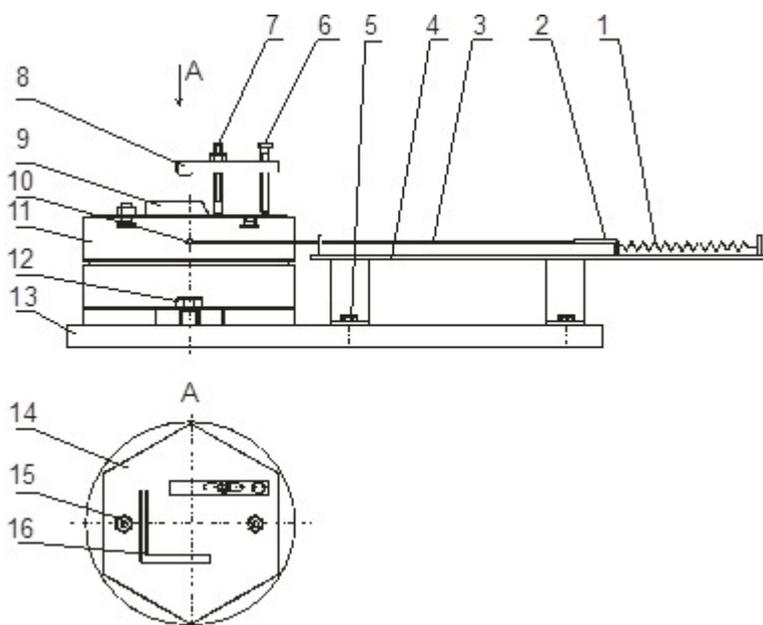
Экспериментальная установка: 1 — пружина; 2 — ползун; 3 — трос; 4 — планка; 5 — основание; 6 — болт; 7 — гайка; 8 — консоль; 9 — угол; 10 — болт; 11 — поворотный стол; 12 — болт; 13 — основание; 14 — пластина; 15 — болт
